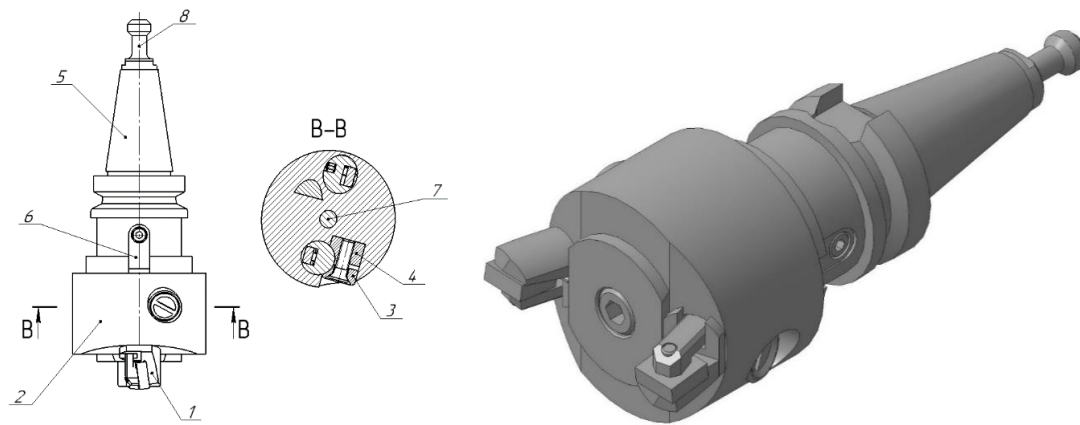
Конструктивная схема и 3D модель зенкера
